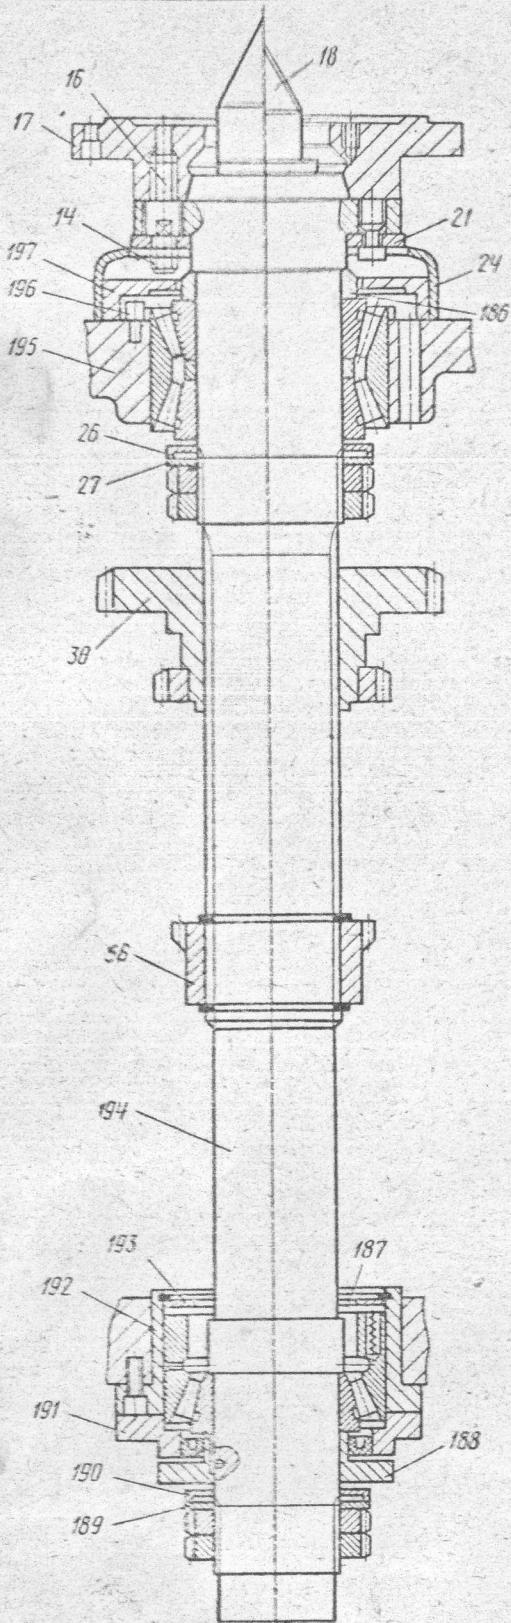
Шпиндельная бабка (чертеж шпинделя в сборе)
